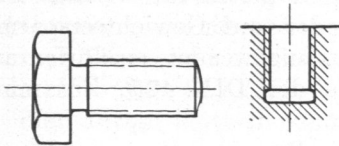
und 343. Schraube mit Rille, DIN 76, Gewindeloch mit Hinterdrehung, DIN 2352.
